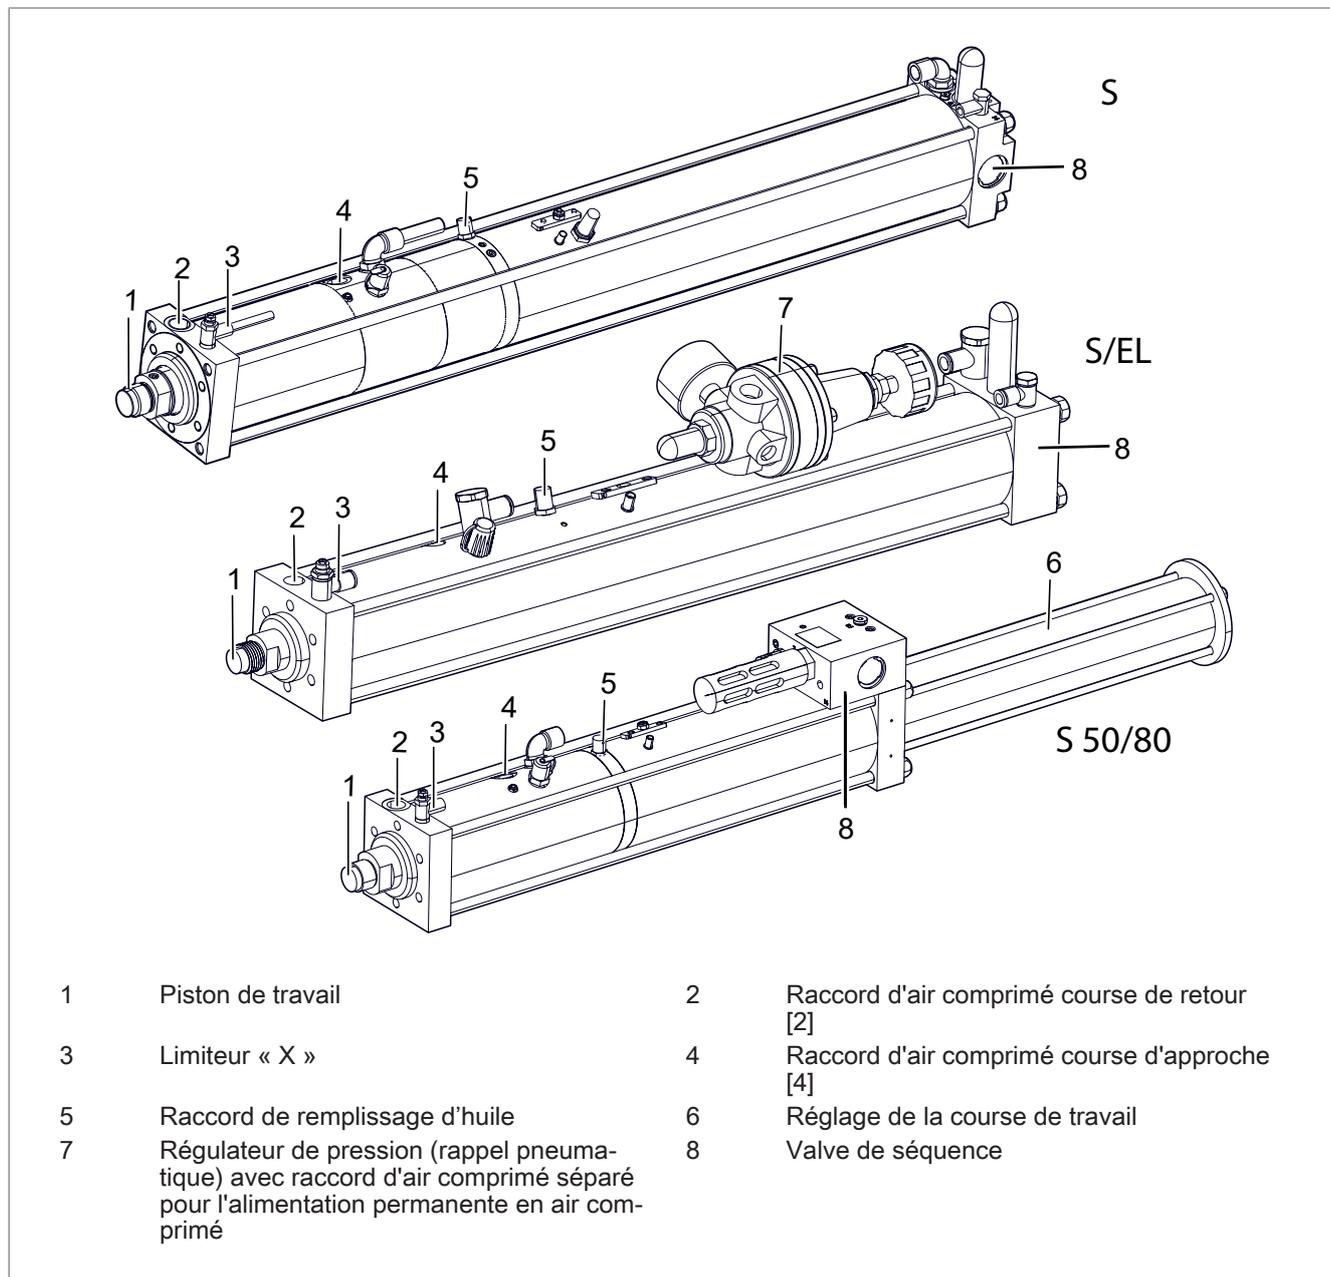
Vue d'ensemble du modèle S, EL, S, version 50/80
